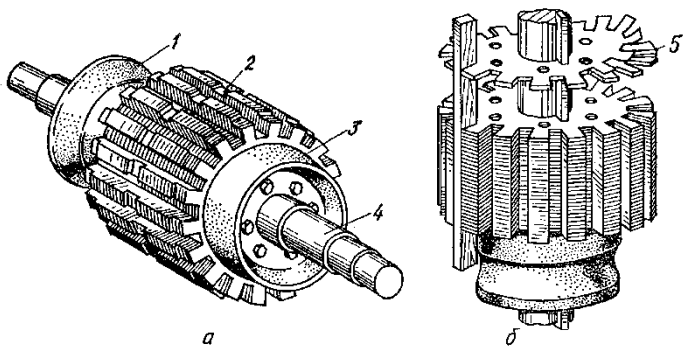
Осердя якоря (а) і процес його збирання (б); 1, 3 - натискні шайби; 2 - виточки для накладання бандажу; 4 - місце для пресування колектора; 5-ізопшійна плівка; 6 - сталевий лист.
